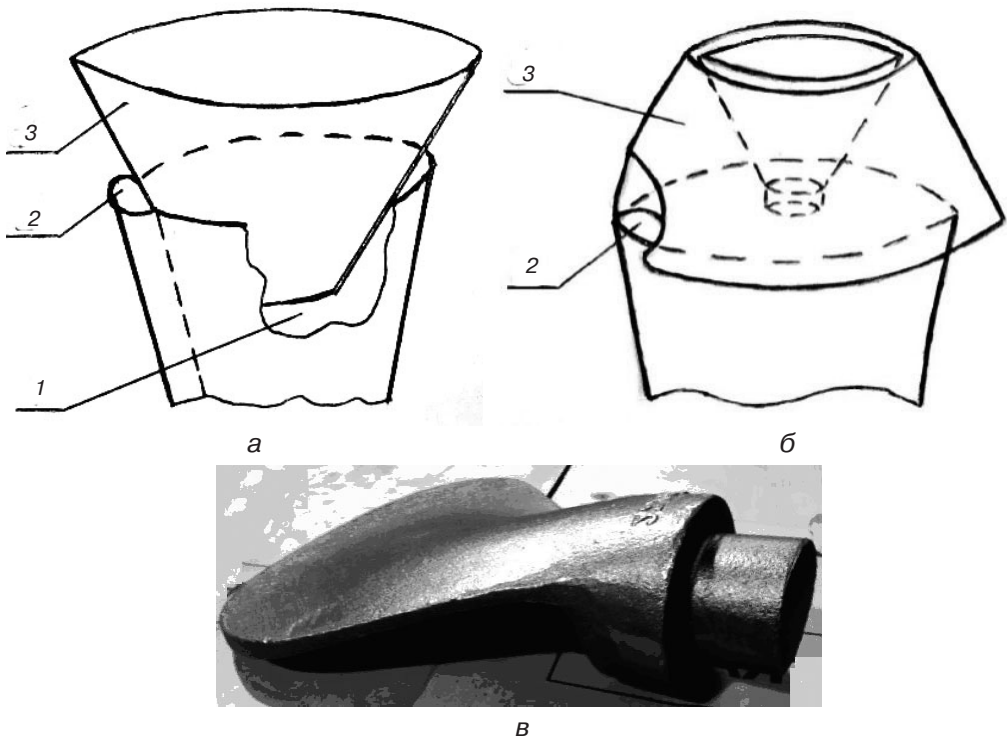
Схемы заливки через приставную воронку (а, б) и пример отливки лопасти (в)
